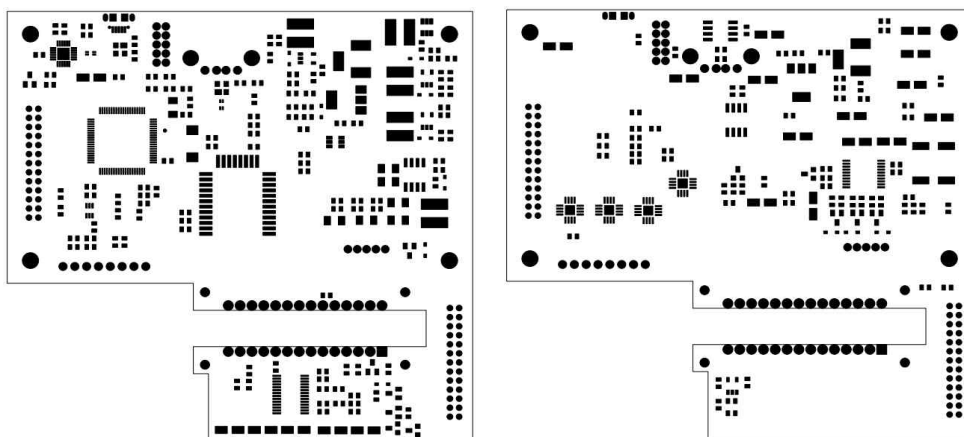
Top(좌) & Bottom(우) 부품배치도에 대한 Drawing 이미지
